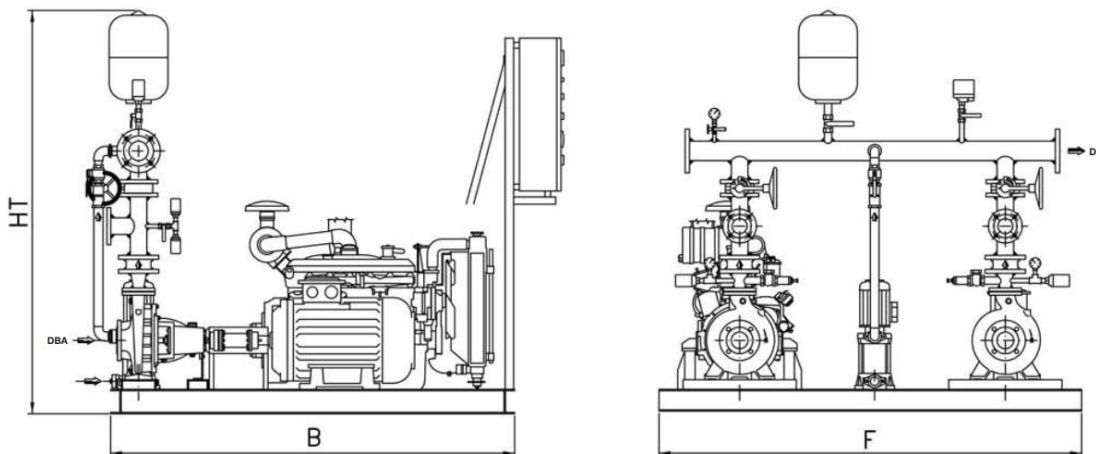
Dimensiones del grupo de bombeo. Fuente: EBARA
